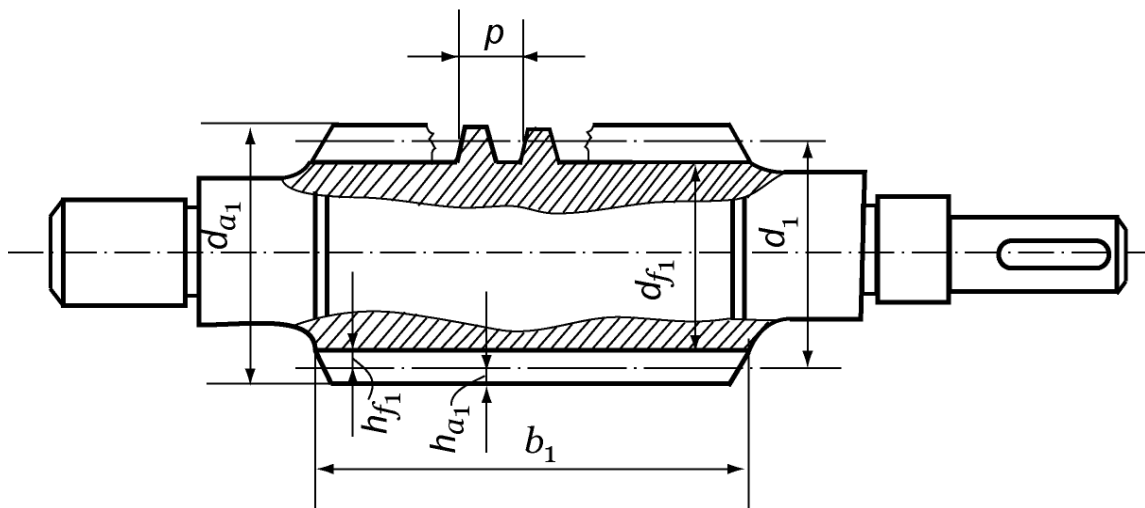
Основні геометричні розміри циліндричного черв'яка:
